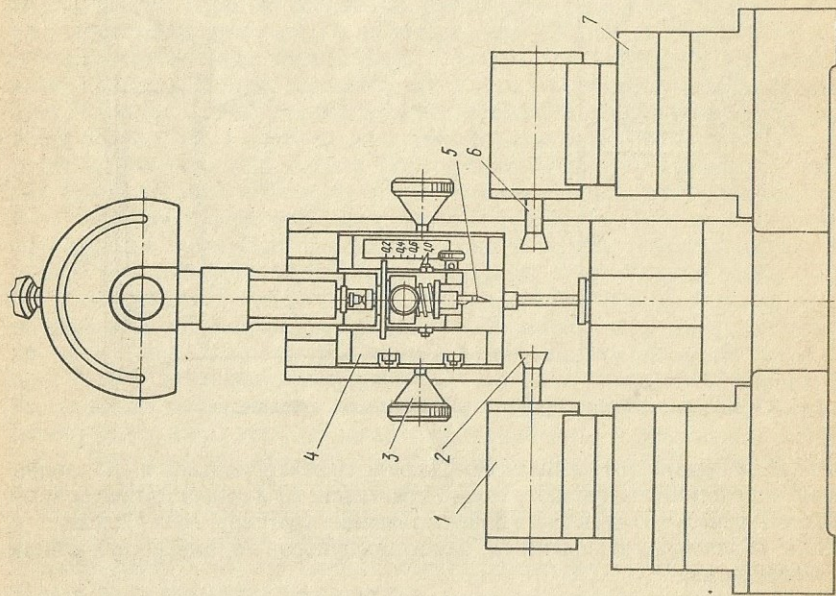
Контрольное устройство для сортировки зубчатых колес с числом зубьев $z < 50$
